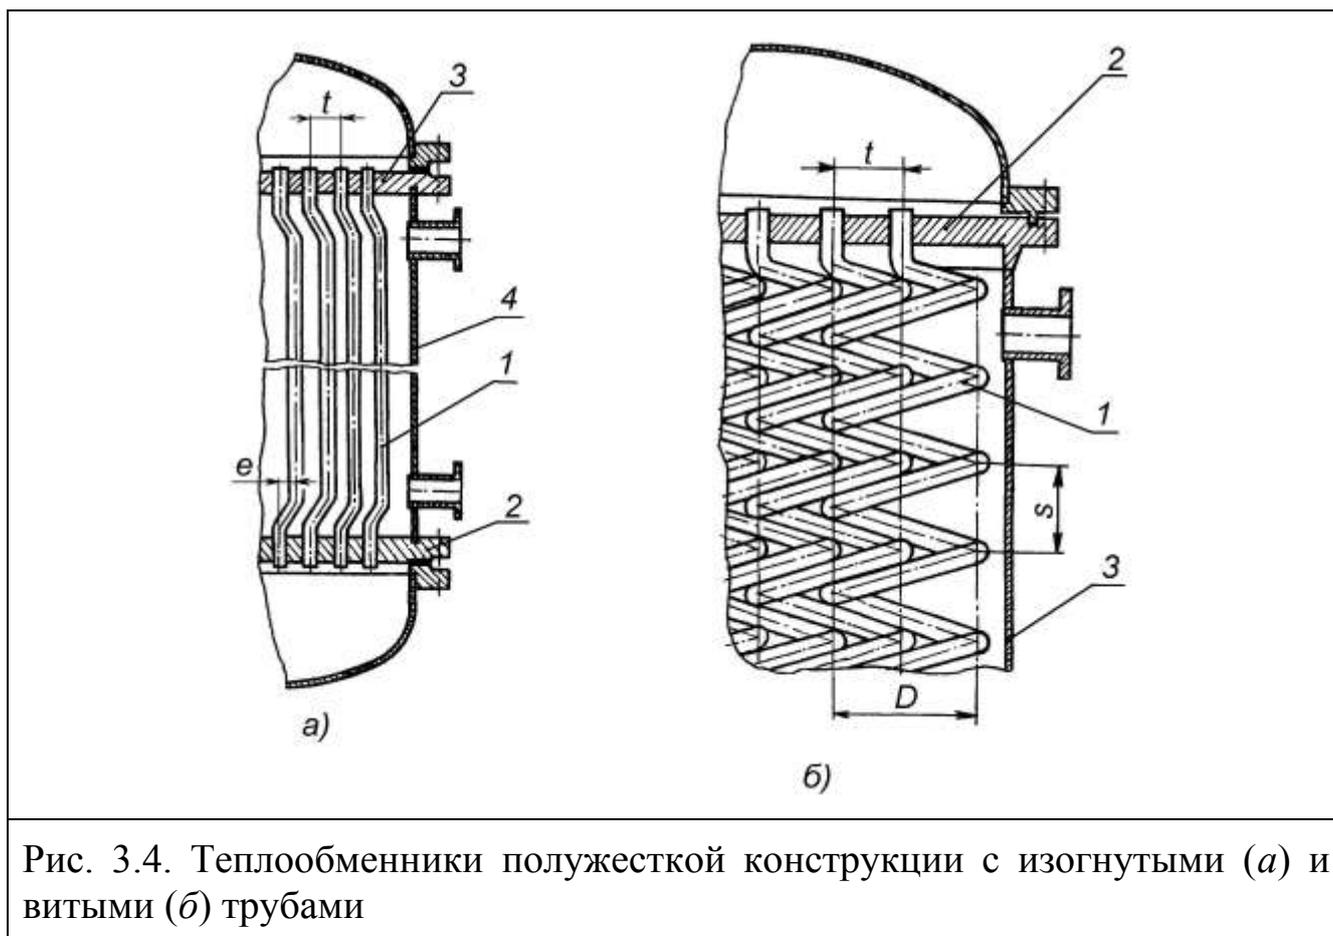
Теплообменники полужесткой конструкции с изогнутыми (а) и витыми (б) трубами
